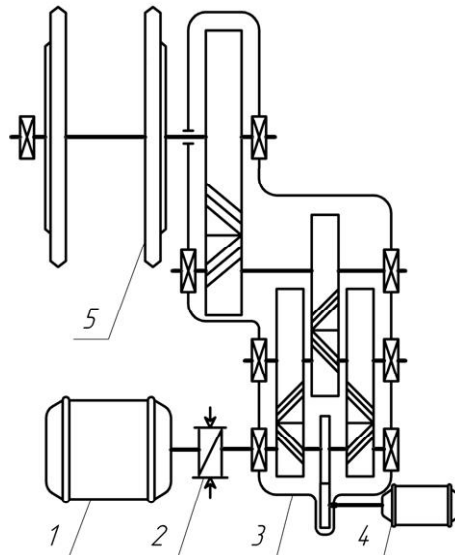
Схема ПГТЭ ЭТ-2(М), ЭТ-3(М): 1 – главный электродвигатель; 2 – рабочие тормоза и тормозная муфта; 3 – редуктор главного привода; 4 – вспомогательный электродвигатель с редуктором; 5 – главный вал с тяговыми звездочками и аварийным тормозом
